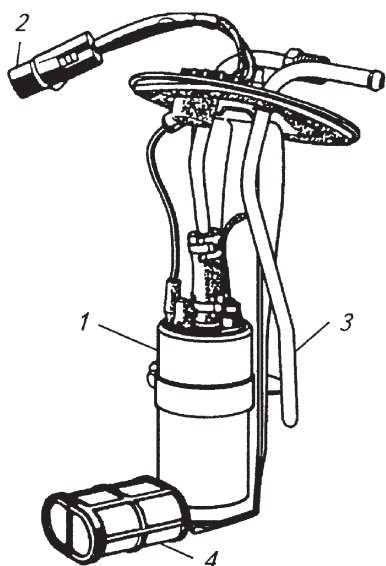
Топливный насос, устанавливаемый в топливном баке:
